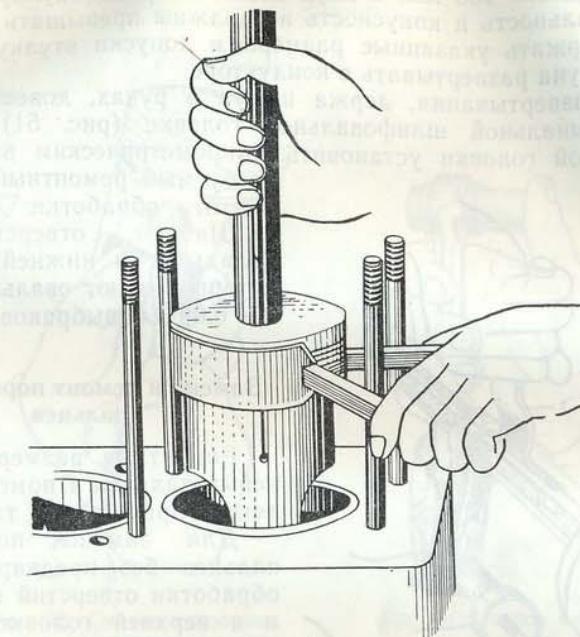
Приспособление для установки поршня с кольцами в цилиндр
